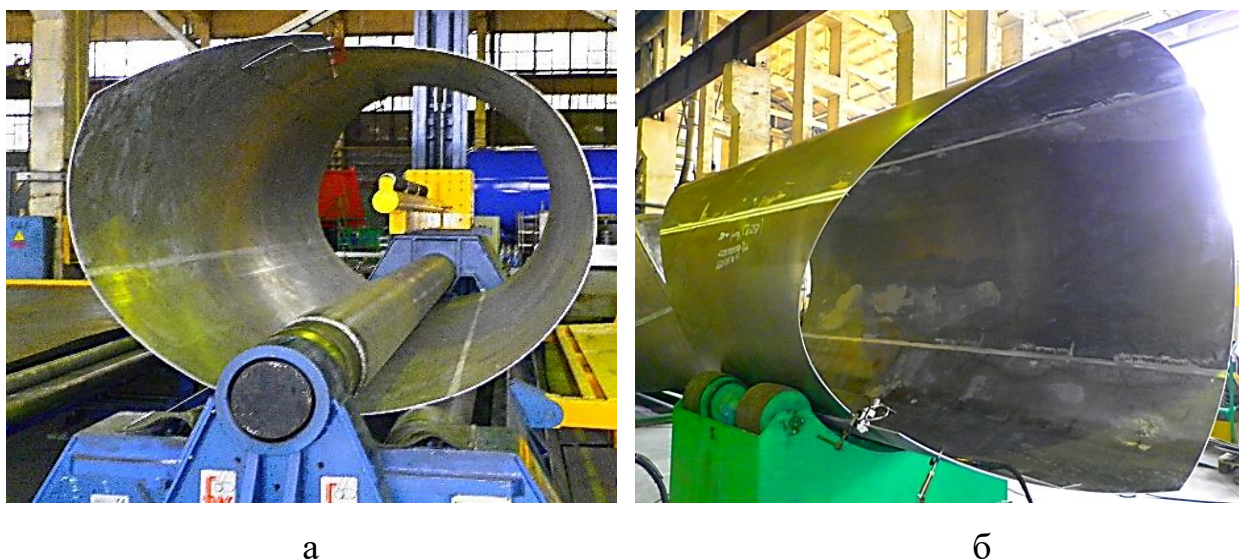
Процесс гибки обечайки цементовоза из сварного полотнища (а) и обечайка после гибки (б)
